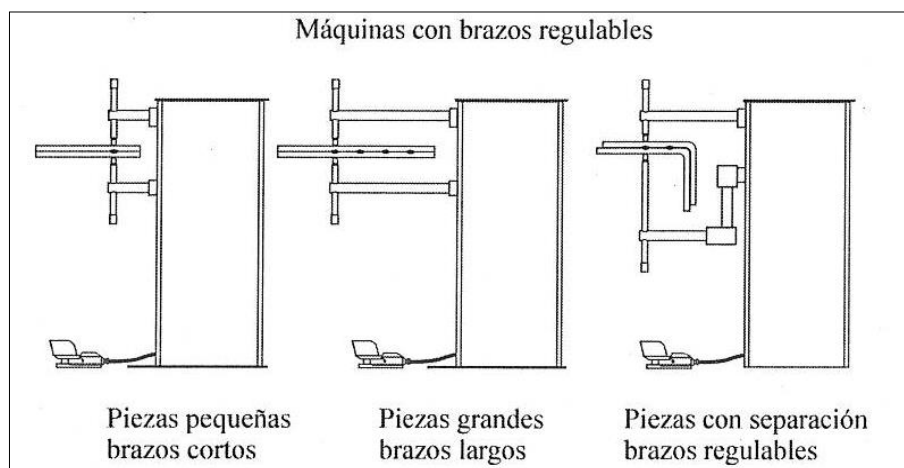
Máquinas de soldadura por resistencia con brazos regulables.
